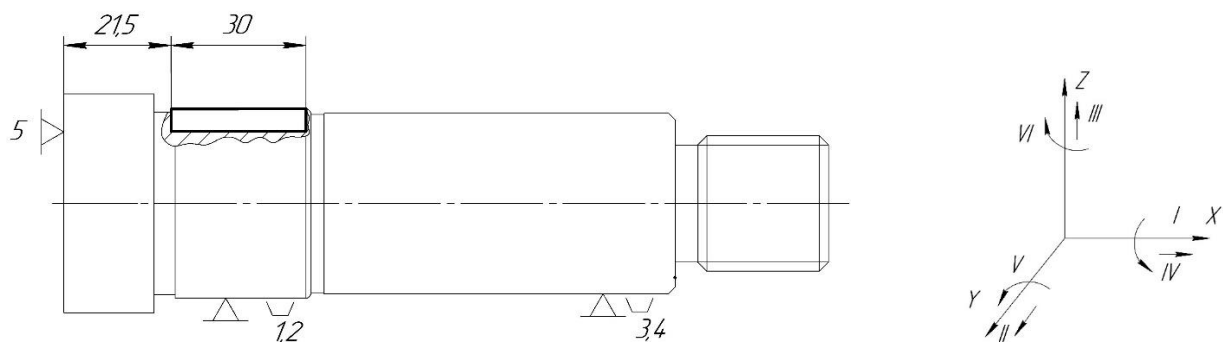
Схема базування та закріплення заготовки на операцію 030 Вертикально-фрезерну з ЧПК
